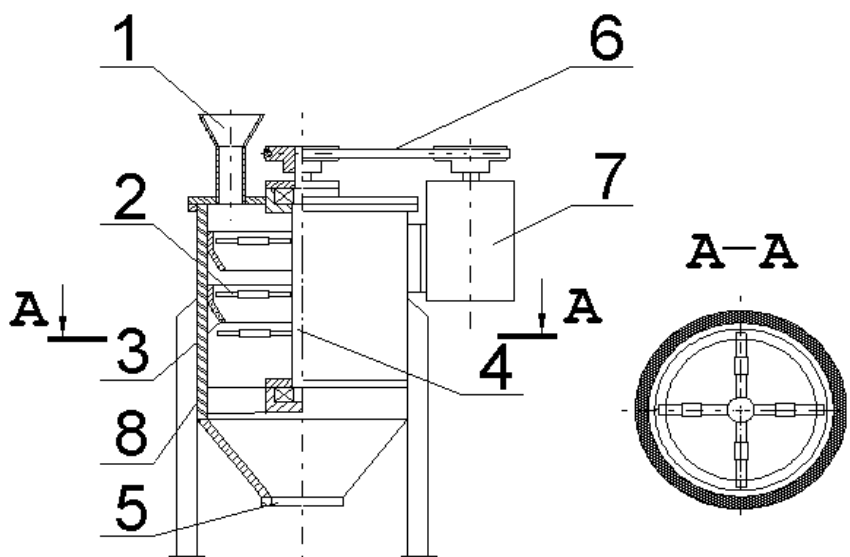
Дробильная установка и схема конструкции дробилки: 1 – загрузка; 2 – ударные элементы; 3 – отражатель; 4 – вертикальный вал; 5 – выгрузочное окно; 6 – ременная передача; 7 – электродвигатель; 8 – корпус
